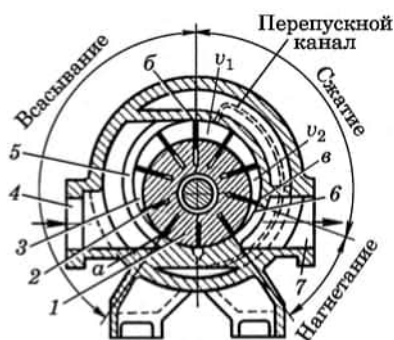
Схема ротационного компрессора с катящимся ротором: а-б — полость всасывания; б-в — полости нагнетания; 1 — ротор, насаженный на вал; 2 — пластины; 3 — полость сжатия; 4 — всасывающий патрубок; 5 — цилиндр; 6 — нагнетательная плоскость компрессора; 7 — нагнетательный патрубок
